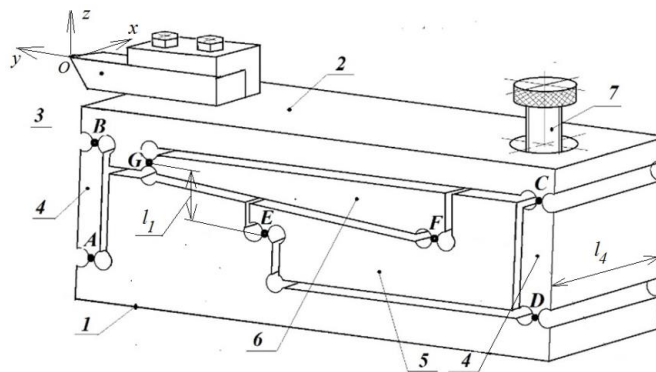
Конструктивна схема різцетримача для прецизійного позиціонування різального інструменту
